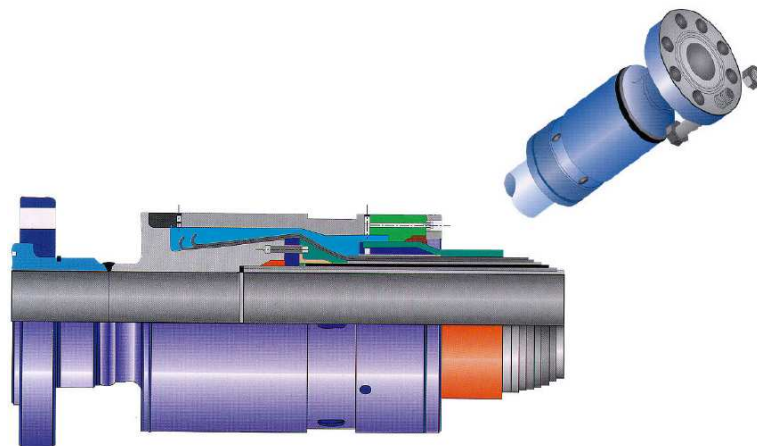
Típico terminal conector do fabricante Technip. (Fonte: Technip)
